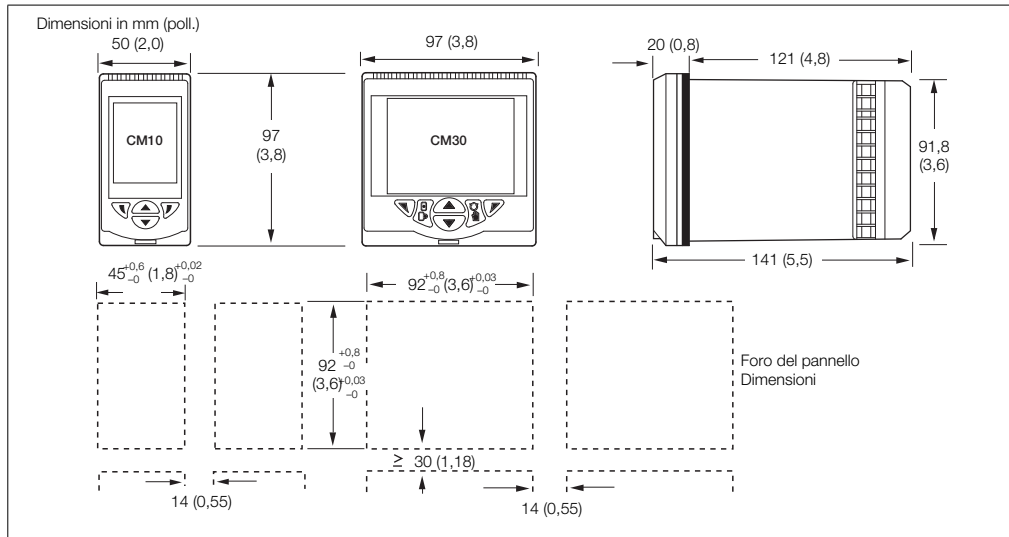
Dimensioni ControlMaster CM10 e CM30
